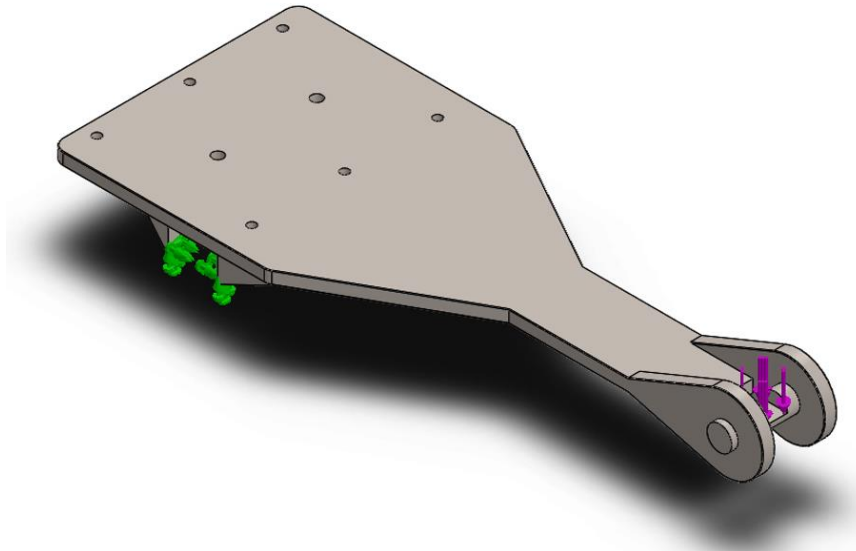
Representação da base de fixação e plano de aplicação da carga no braço de apoio.
